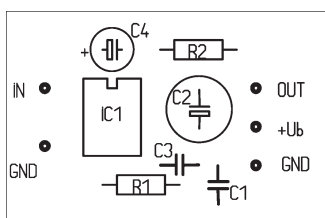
Zapojení zesilovače s obvodem LM386 se zesilením = 50
